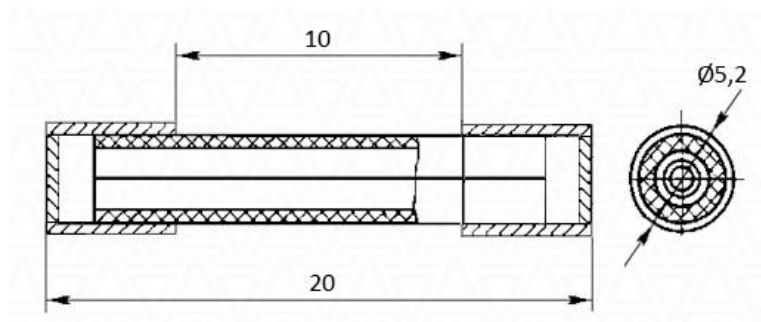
Габаритні розміри запобіжника AFU-T-06-0.16 A-250B "
